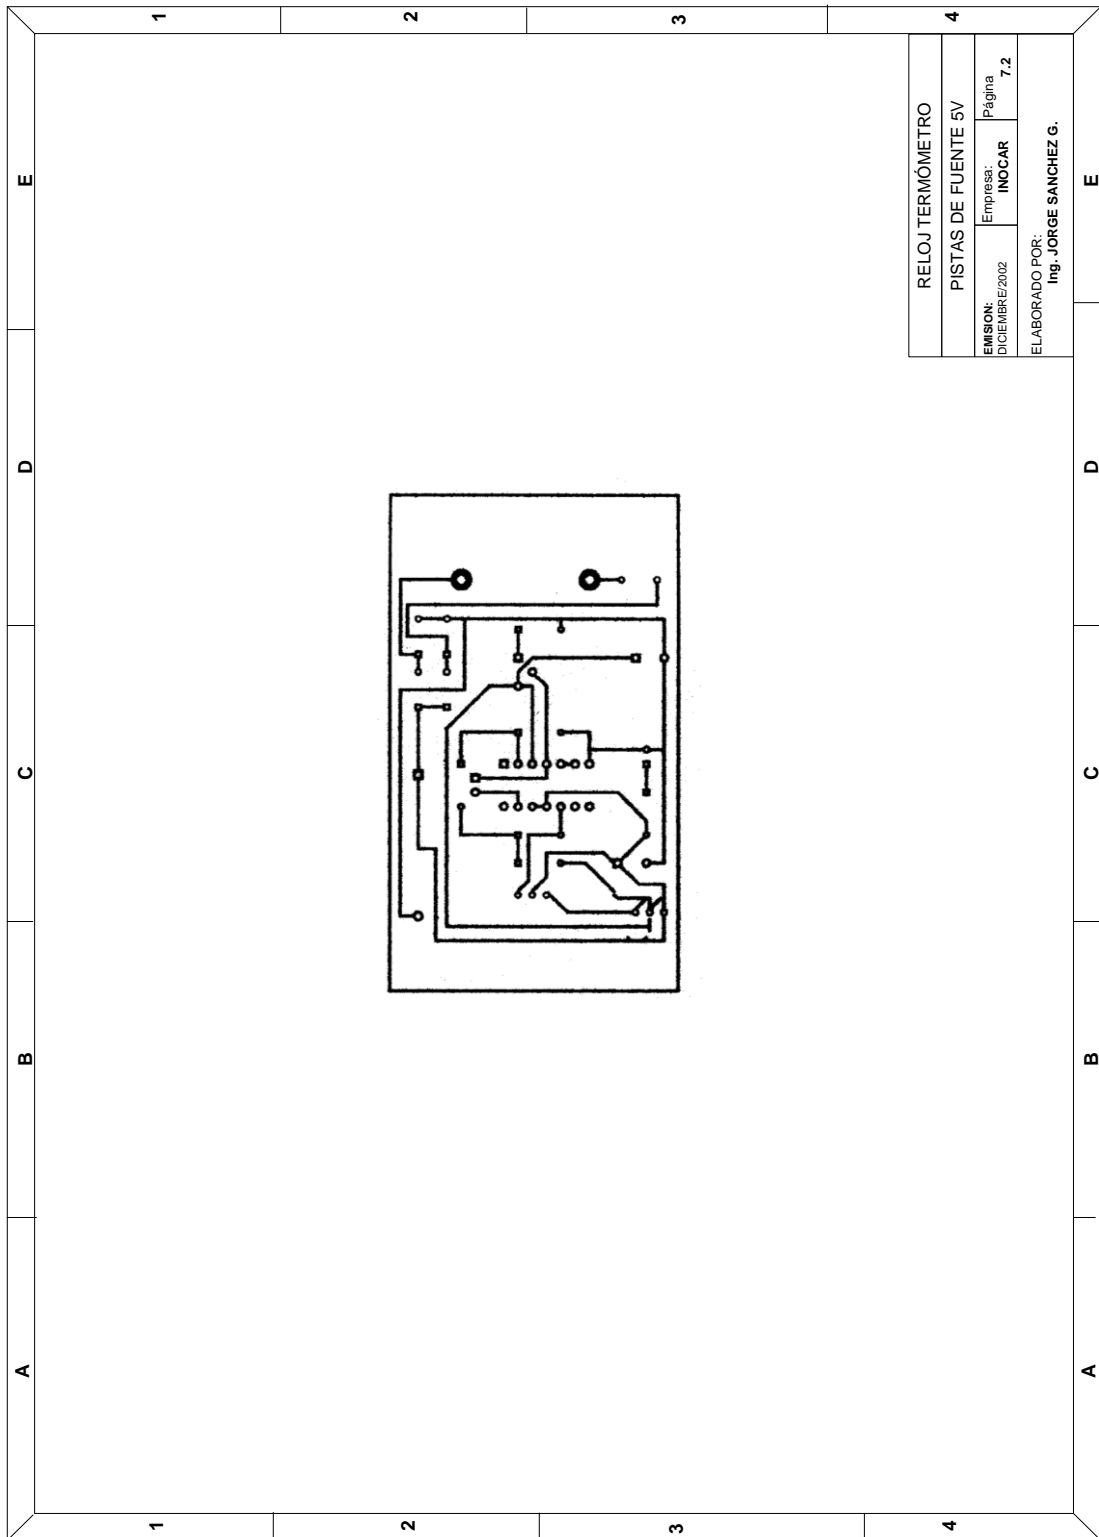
Tarjeta de fuente 5VDC (Diagrama de pistas lado de soldadura)
